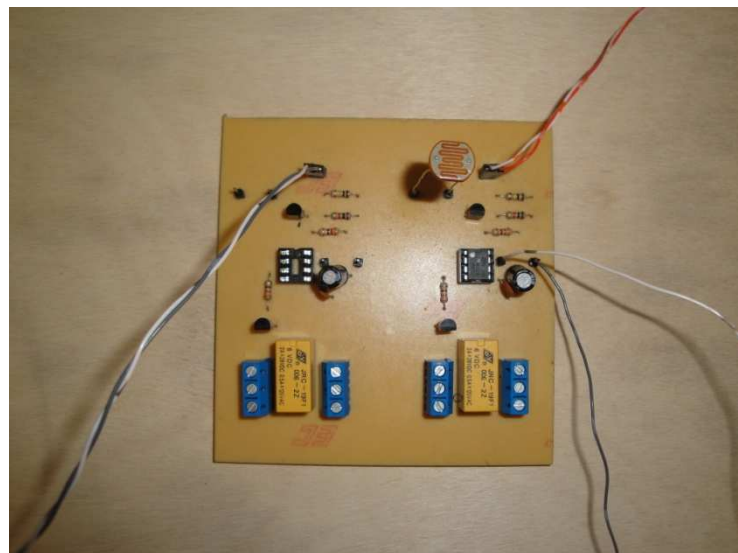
Placa de circuito impreso del proceso de clasificación con sus elementos soldados.
